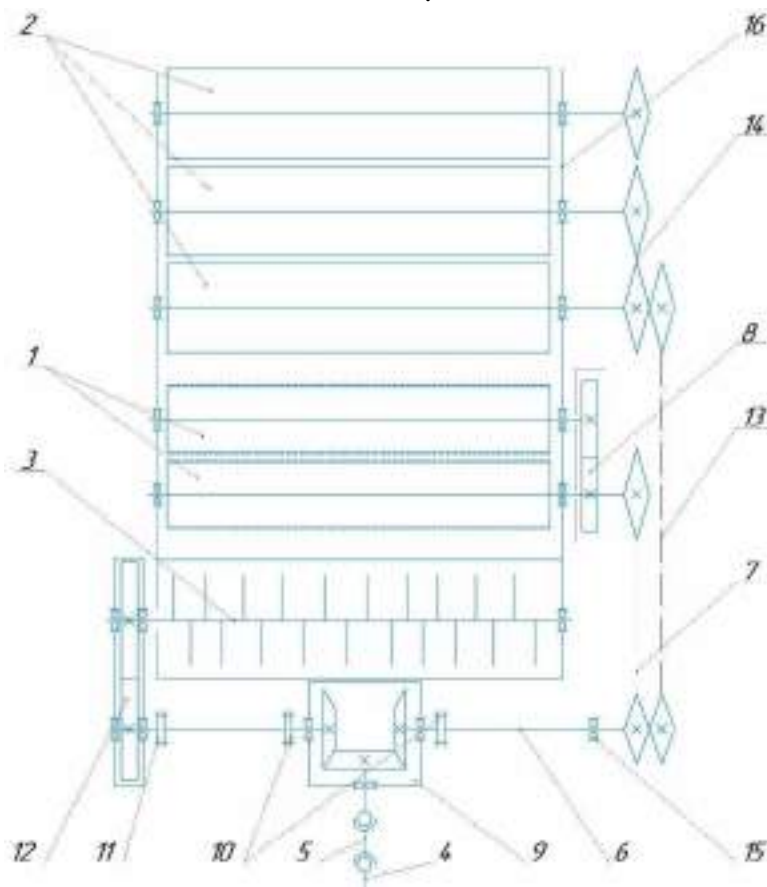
Кінематична схема приводу робочих органів машини : 1 – Подрібнювач вальцевий; 2 – вальці подаючі; 3 – фреза; 4 – ВВП трактора; 5 – карданний вал; 6 – вал приводу подрібнювача і подаючих вальців; 7 – ланцюгова передача приводу подрібнювача; 8 – циліндрична зубчаста передача; 9 – конічний редуктор; 10 – муфта запобіжна; 11 – муфта з'єднувальна; 12 – редуктор бортовий; 13 – ланцюгова передача приводу подаючих вальців; 14 – ланцюгова передача вальців; 15 – підшипниковий вузол; 16 – корпус
